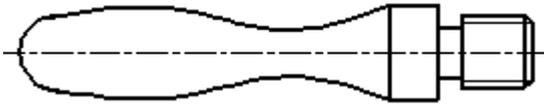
Образец оформления плавного перехода от одной поверхности к другой
